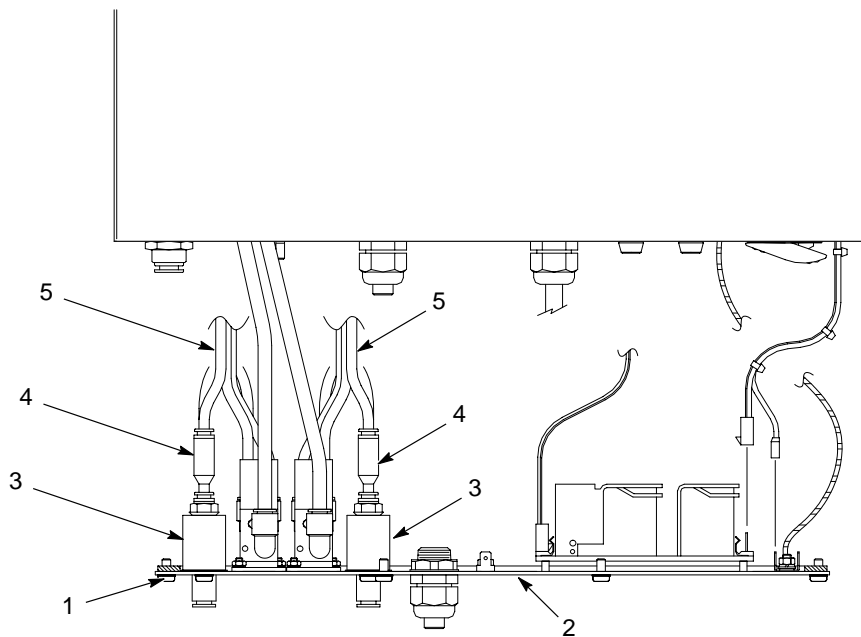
Remplacement du câble du pistolet de poudrage
